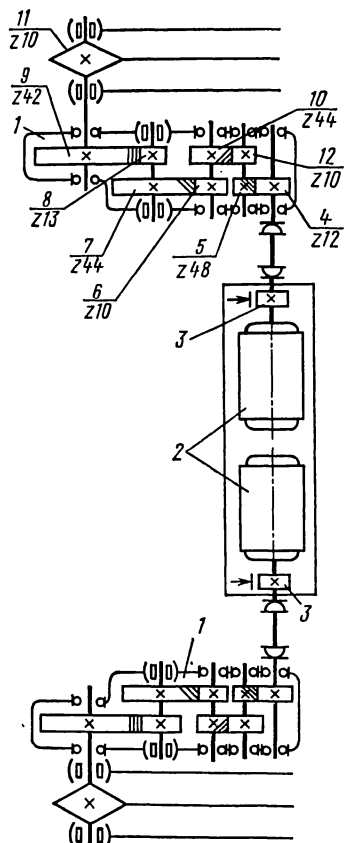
Кинематическая схема механизма передвижения крана ДЭК-251:
